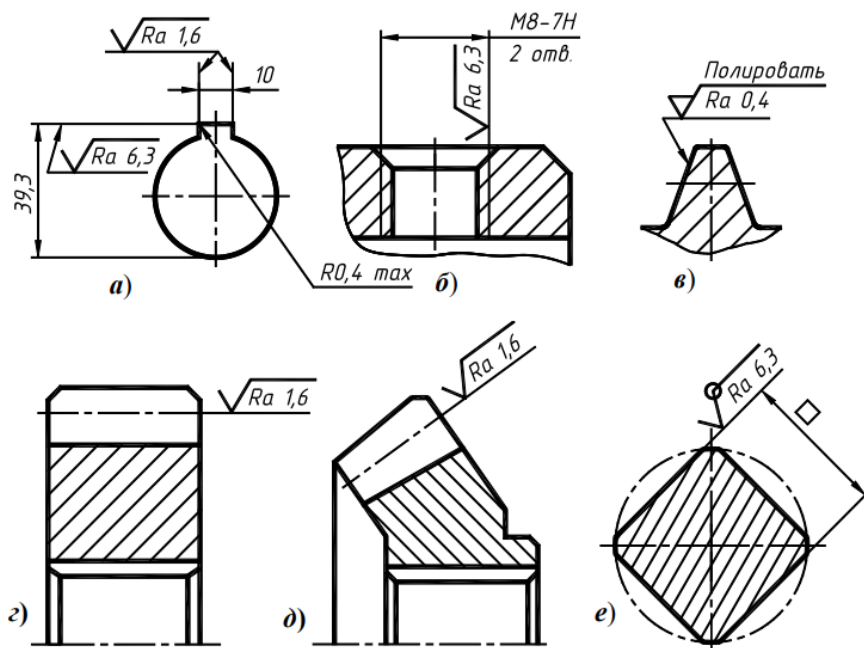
Шероховатость поверхности резьбы и зубьев
